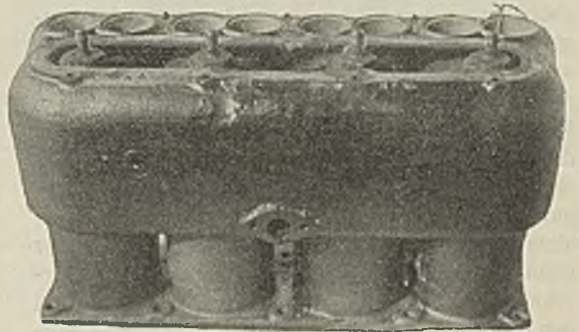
Automobilzylinder, fertig geschweißt.
